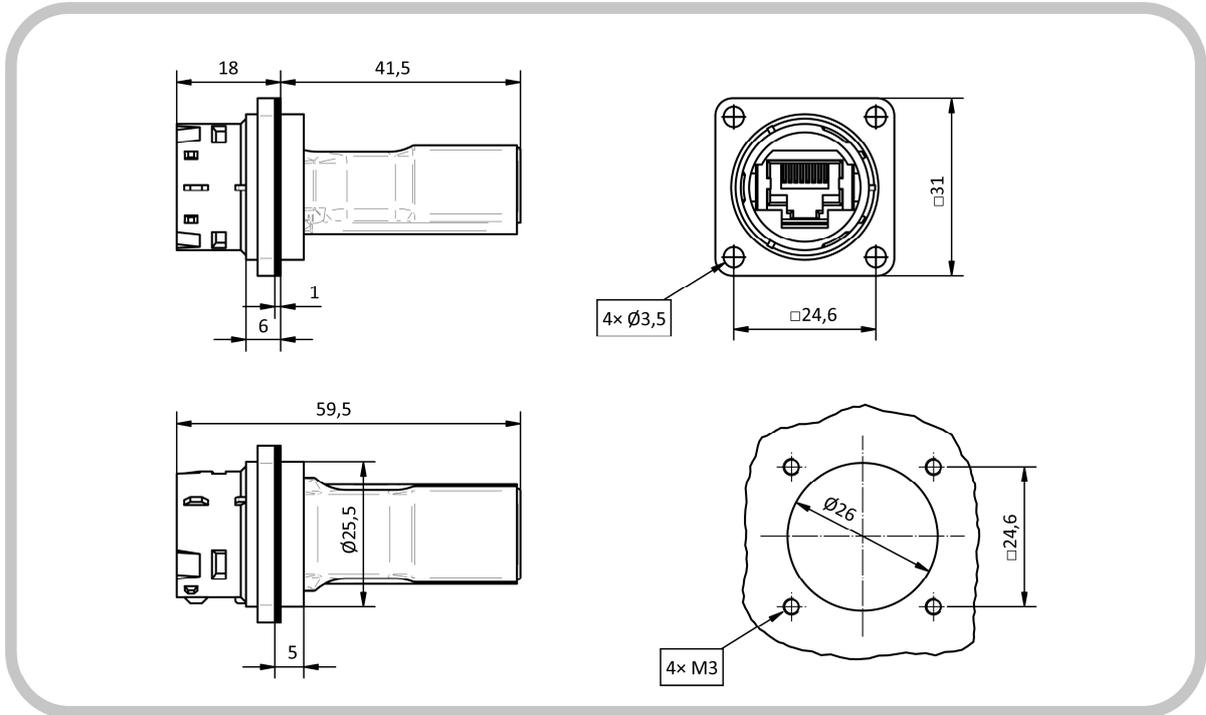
Maßzeichnung für EN-10HG und EN10H
